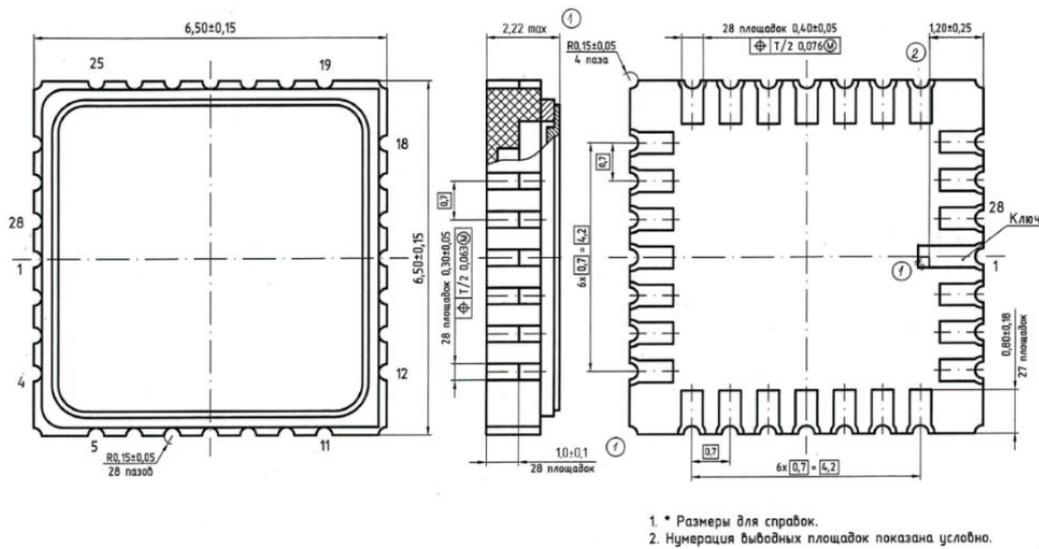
Габаритный чертеж корпуса 5123.28-1.01 (размеры в мм)
